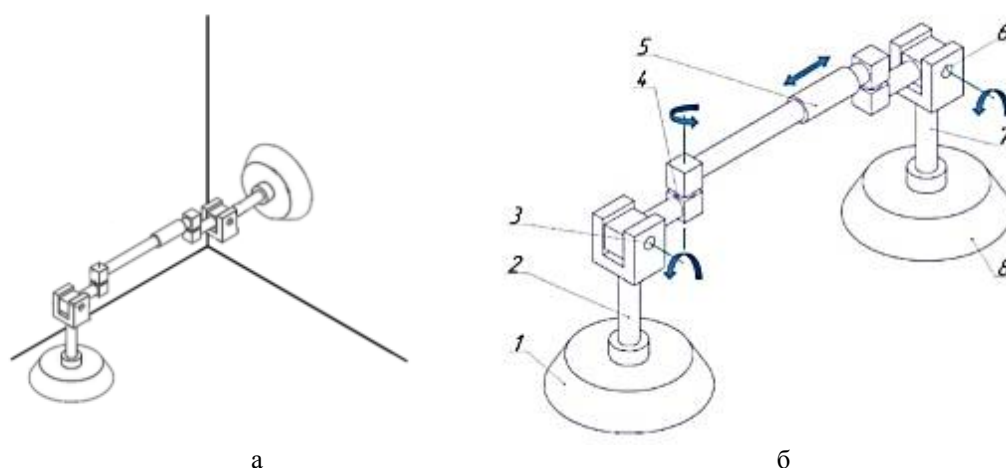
Макет двухопорного ШРВП: а – принцип перехода на сопряженную поверхность; б – конструктивная схема
